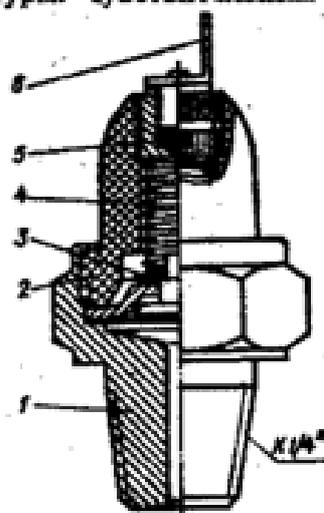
Датчик давления масла ММ 111Д: 1 - корпус; 2 - изолятор; 3 - контакт; 4 - пружина; 5 - фильтр; 6 - штеккер
